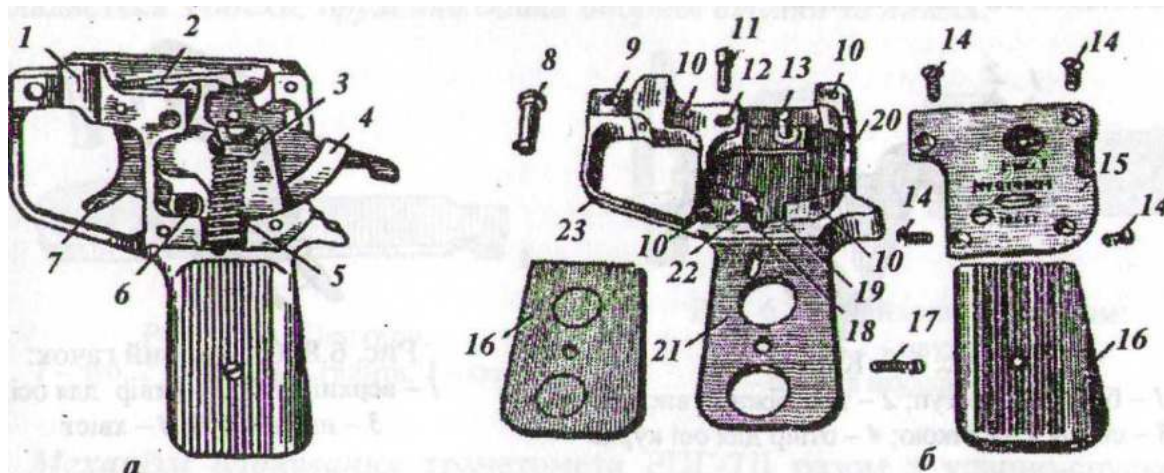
Ударно-спусковий механізм! *а* - УСМ (у зібраному вигляді); *б* - корпус УСМ (у розібраному вигляді); *1* - корпус; *2* - шептало; *3* - стрижень; *4* - курок; *5* - бойова пружина; *6* - запобіжник; *7* - спусковий гачок; *8* - чека; *9* - отвір для чеки; *10* - нарізні отвори для гвинтів кришки; *11* - вісь спускового гачка; *12* - отвір для осі спускового гачка; *13* - вісь курка; *14* - гвинти кришки; *15* - кришка; *16* - щічки; *17* - з'єднувальний гвинт; *18* - паз для вибивана; *19* - гніздо для бойової пружини; *20* - виріз для курка; *21* - пластина; *22* - отвір для запобіжника; *23* - запобіжна скоба
